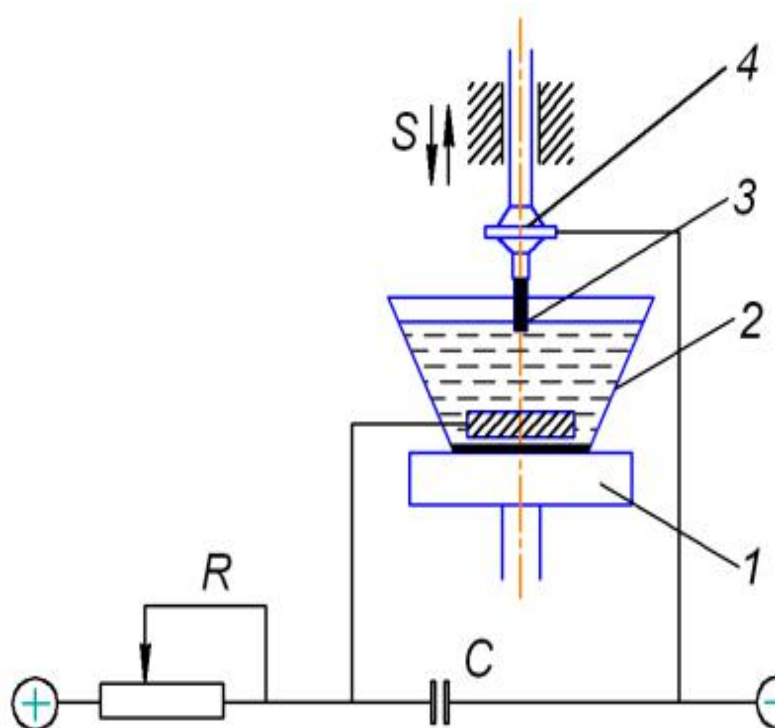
Принципова схема верстата для електроіскрової обробки ЛКЗ-57
